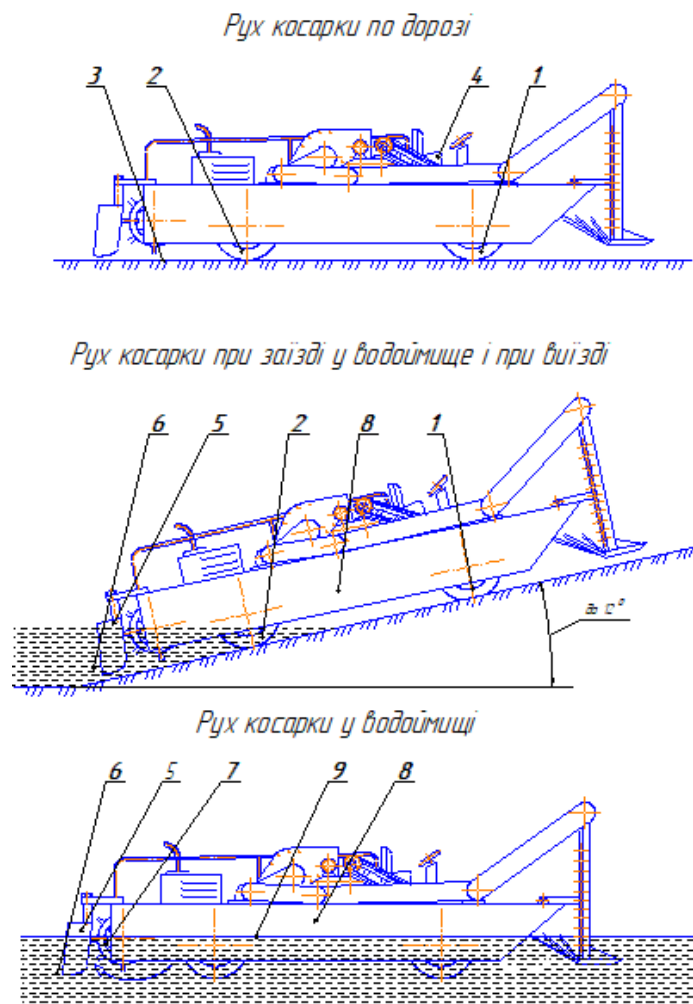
Схеми руху косарки. 1 – Приводні колеса; 2 – Колеса керування; 3 – Дорога; 4 – Місце керування; 5 – Кермо керування напрямом руху на воді; 6 – Водоймище; 7 – Водяний рушій; 8 – Плавзасіб; 9 – Ватерлінія.
